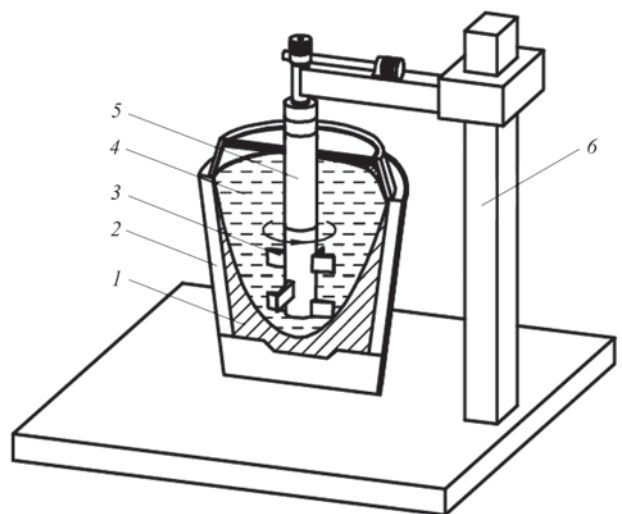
Вид пристрою для механічного перемішування рідкої серцевини зливка: 1 — затверділий метал; 2 — виливниця; 3 — лопатки; 4 — рідкий метал; 5 — вал; 6 — стійка з механізмами кріплення та обертання валу
